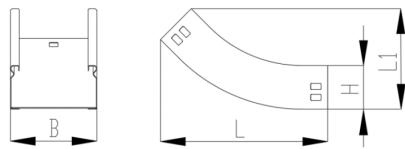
Поворот плавный на 45° вертикальный внутренний
